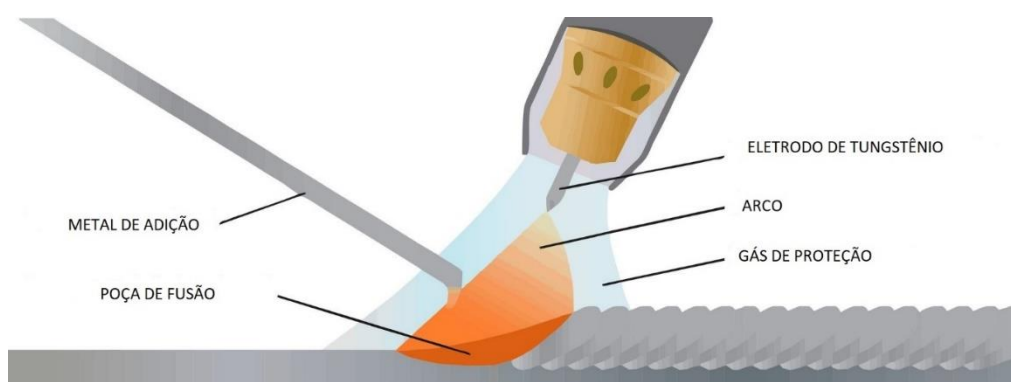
Esquema de soldagem TIG Fonte: Adaptado “O soldador” Ricardo Gomes (2017)
